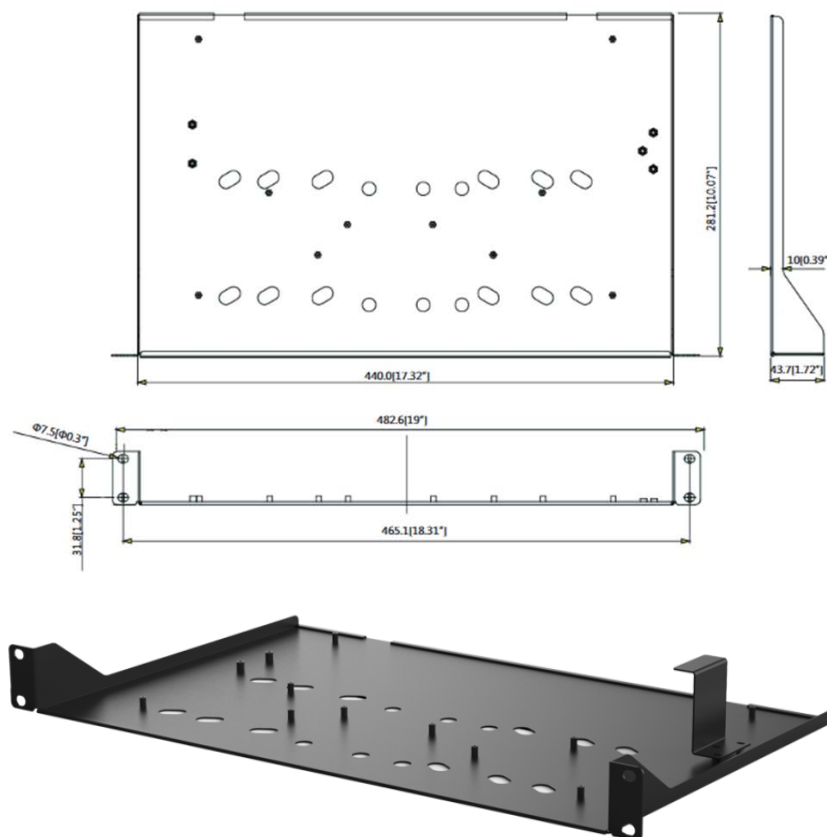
Внешний вид и габариты BOLID BR-111
